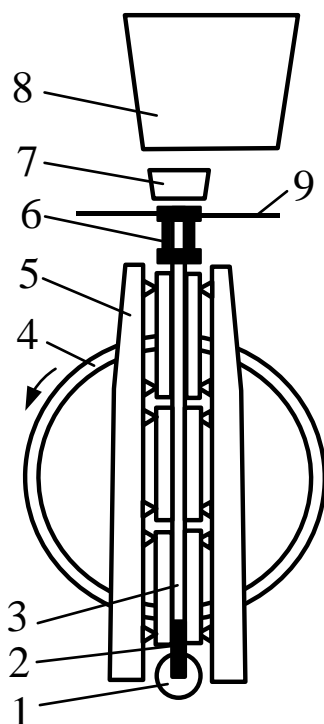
Схема МНПРС: 1 – механизм вытягивания заготовки; 2 – затравка; 3 – слиток; 4 – поворотная рама; 5 – направляющие балки; 6 – кристаллизатор; 7 – разливочное устройство; 8 – сталеразливочный ковш; 9 – разливочная площадка
